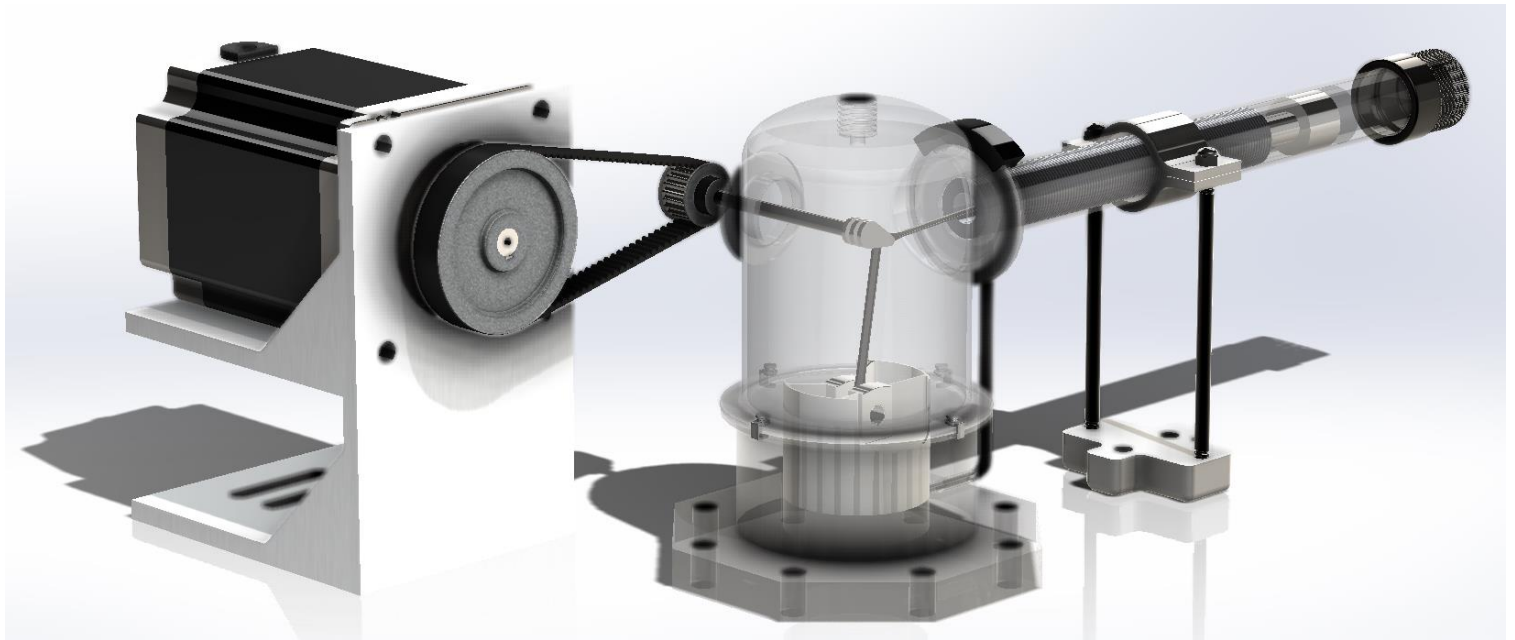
Assembly βάσης στήριξης κυλίνδρου
